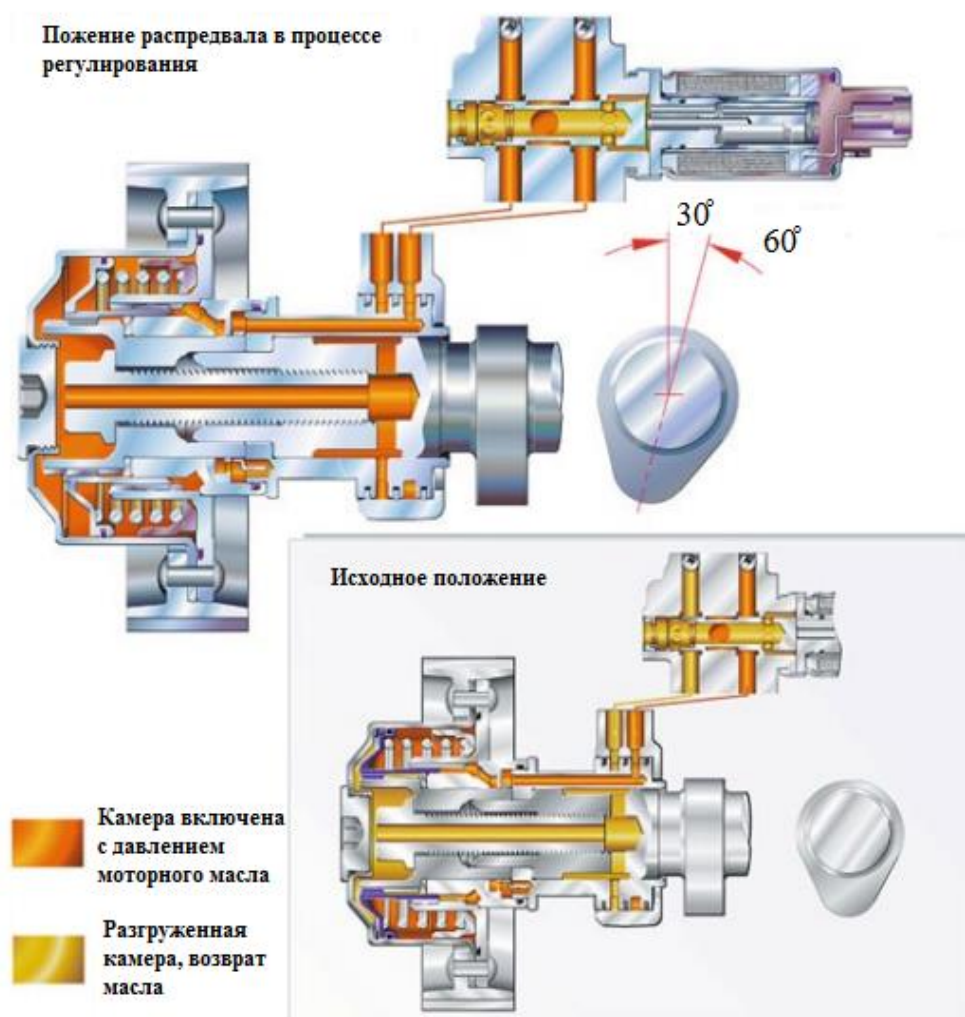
Регулятор поворотного двигателя или лопастной ячейки для цепных приводов
